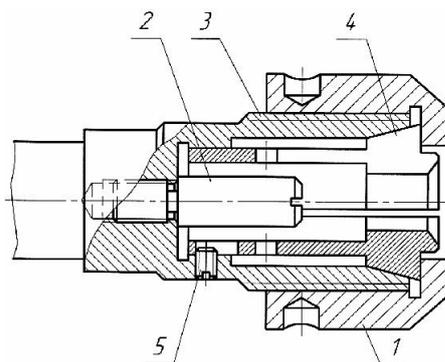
Универсальный цанговый патрон: 1– нажимная гайка;
